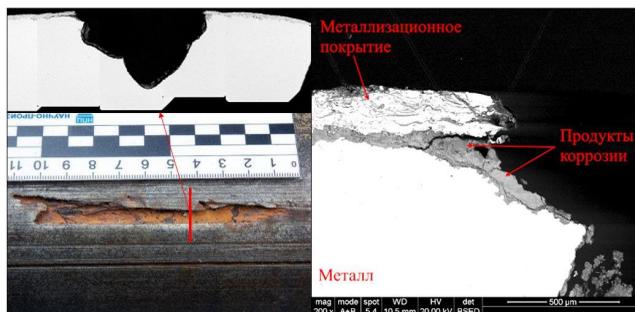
Механические повреждения корпуса ПЭД. Образец №1
